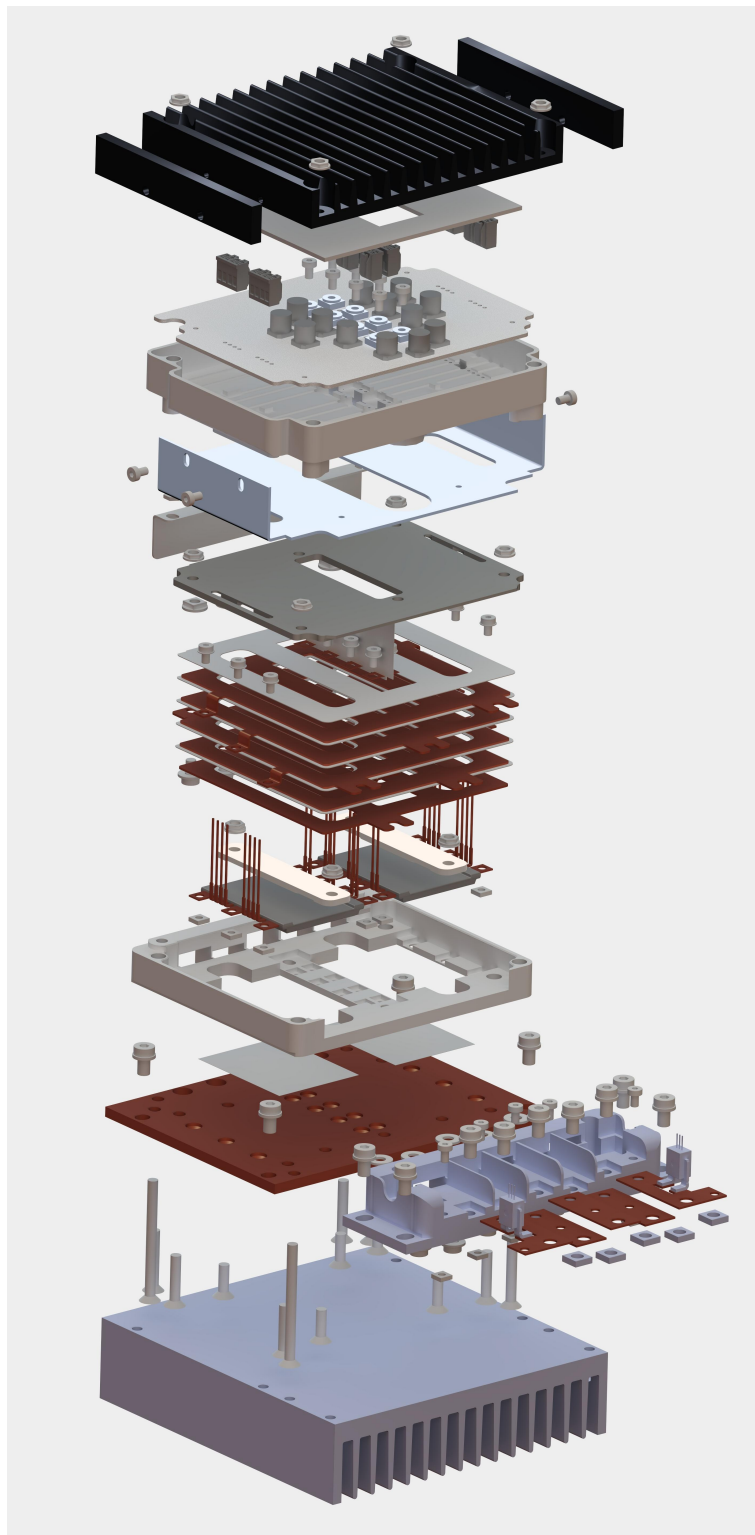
Explosionszeichnung des 5 kVA-Basisumrichters [152]
